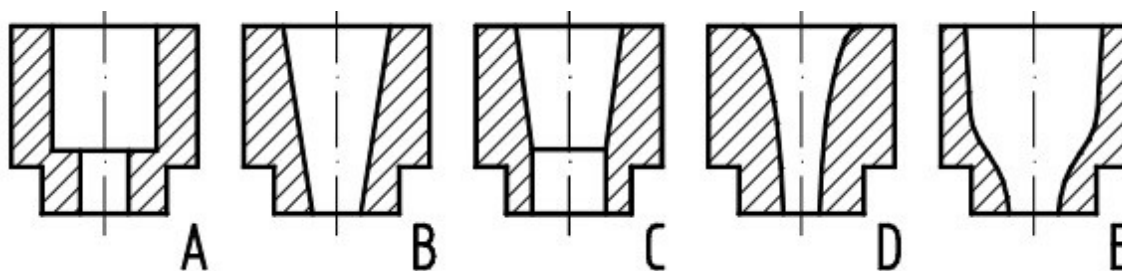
Řezací hlavy pro abrazivní vodní paprsky [31].
